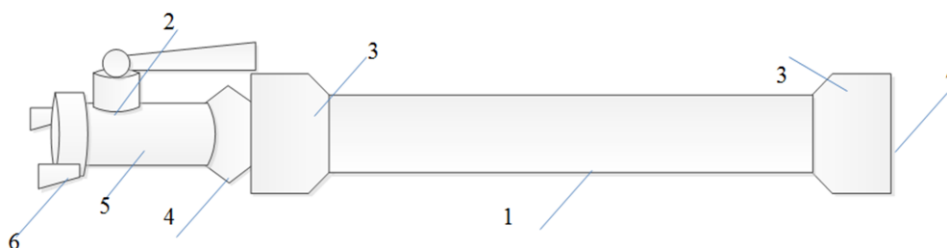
Будова перекидного ствола для отримання повітряно-механічної піни низької кратності: 1 – корпус кожуха (циліндричної форми); 2 – перекидний кран з ручкою; 3 – прогумовані циліндричні накладки; 4 – дифузор; 5 – корпус ствола; 6 – головка рукава діаметром 38 мм; 7 – сітка металева розмірами вічок 1,5x1,5 мм.
